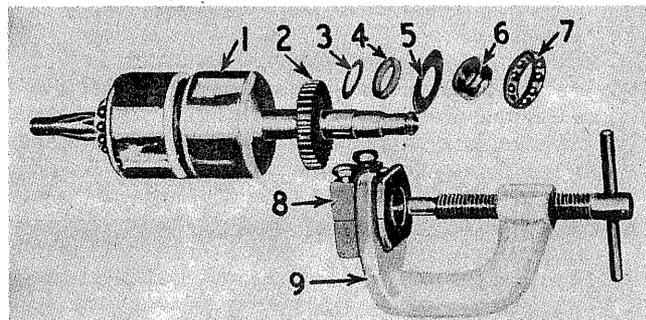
VUE ECLATÉE DES PIÈCES DU ROTOR AVEC L'OUTIL EXTRACTEUR SE-839 POUR LA CAGE INTÉRIEURE DU ROULEMENT. 1 - ROTOR. 2 - PIGNON DU ROTOR. 3 - CALES DU ROTOR. 4 - ENTRETOISE DU ROULEMENT DE L'ARBRE DU ROTOR. 5 - DEFLECTEUR D'HUILE. 6 - CAGE INTÉRIEURE DU ROULEMENT. 7 - ROULEMENT A BILLES ET CAGE. 8 - ADAPTEUR DE LA CAGE DU ROULEMENT. 9 - EXTRACTEUR.
